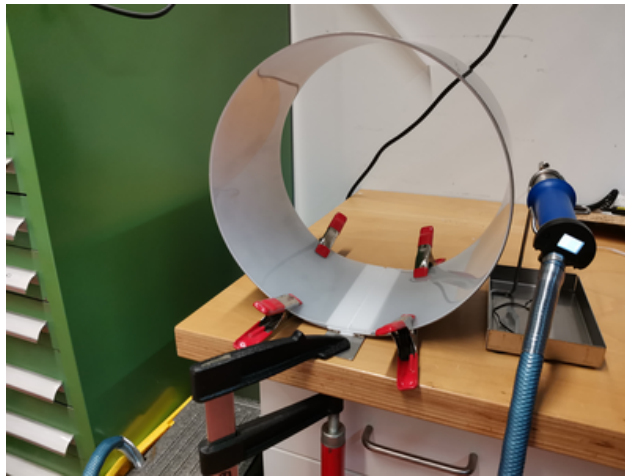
Platte zusammenführen und mit Klammern fixieren. Rechts im Bild: Heißluftgebläse mit Schweißschuh.
